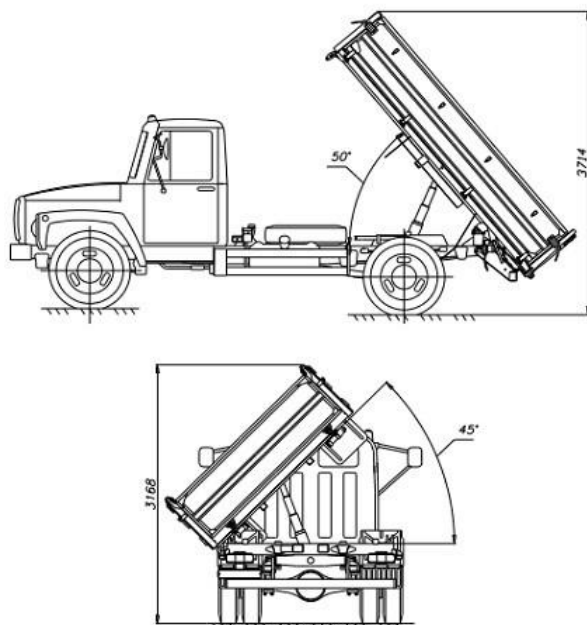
Основные размеры автомобиля- самосвала в рабочих положениях
